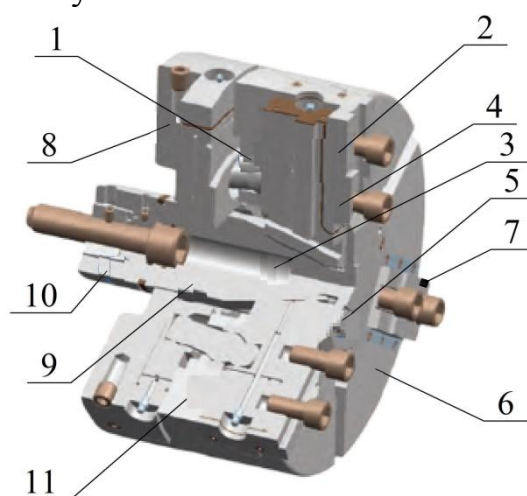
Конструкция современного трехкулачкового патрона с компенсацией центробежной силы для токарного станка с ЧПУ: 1 – корпус; 2 – запирающая крышка; 3 – базовый кулачок; 4 – плоское уплотнение; 5 – прямоугольное уплотнение; 6 – крышка; 7 – скребковые планки; 8 – прямоугольное уплотнение; 9 – груз для компенсации центробежной силы; 10 – поршень
